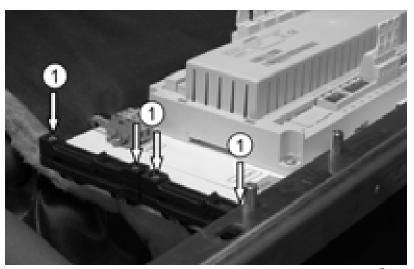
Zugentlastungen mit je zwei Kreuzschlitzschrauben ①
